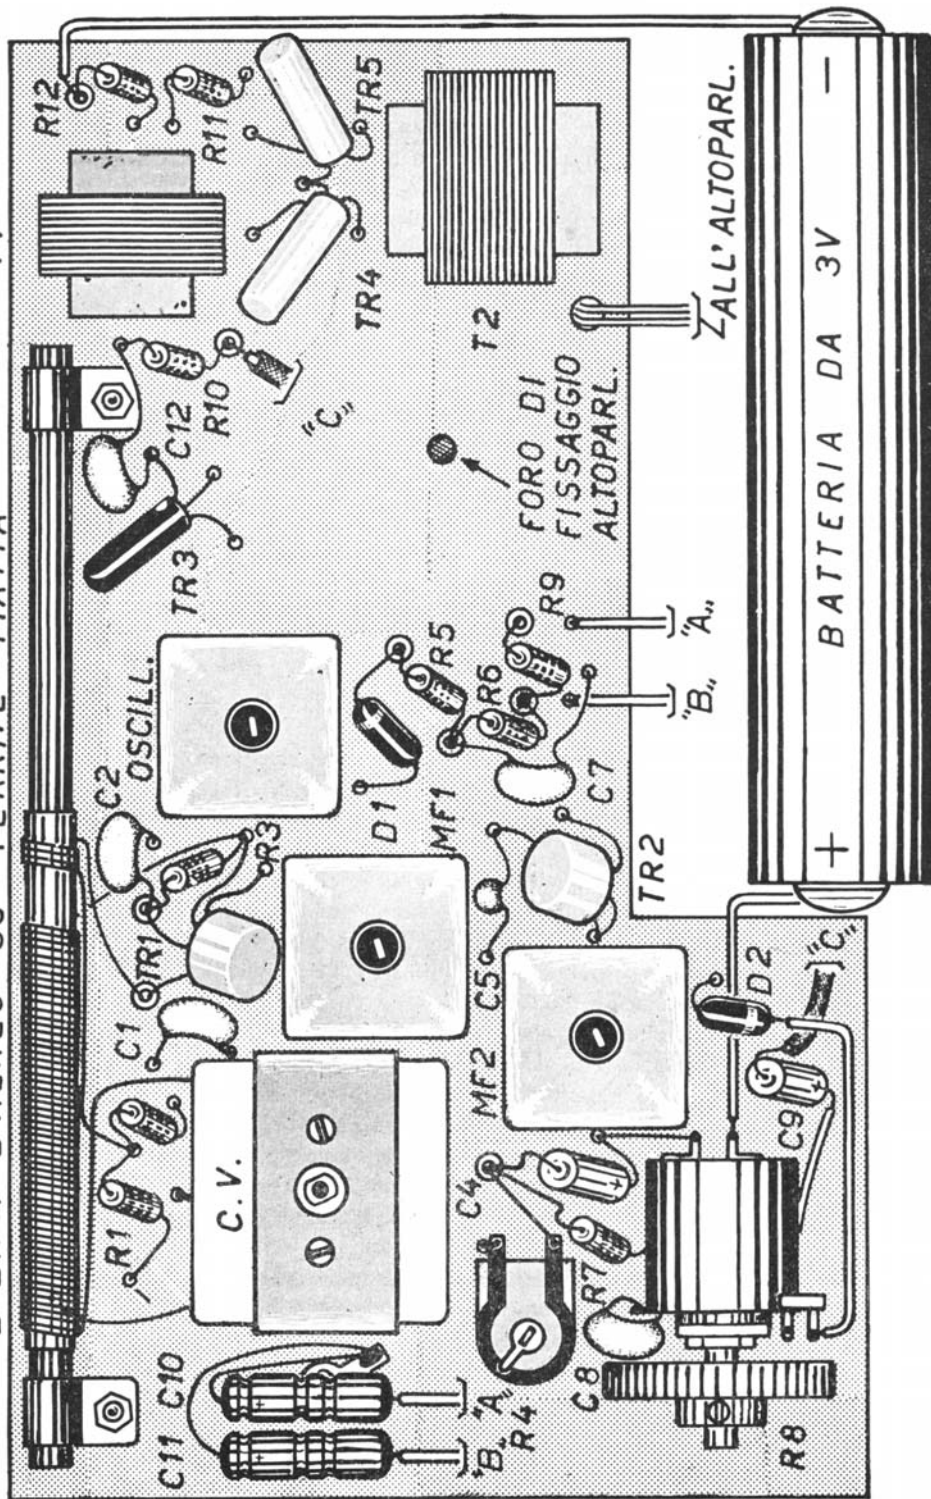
Disposizione dei componenti sul pannello di montaggio.
